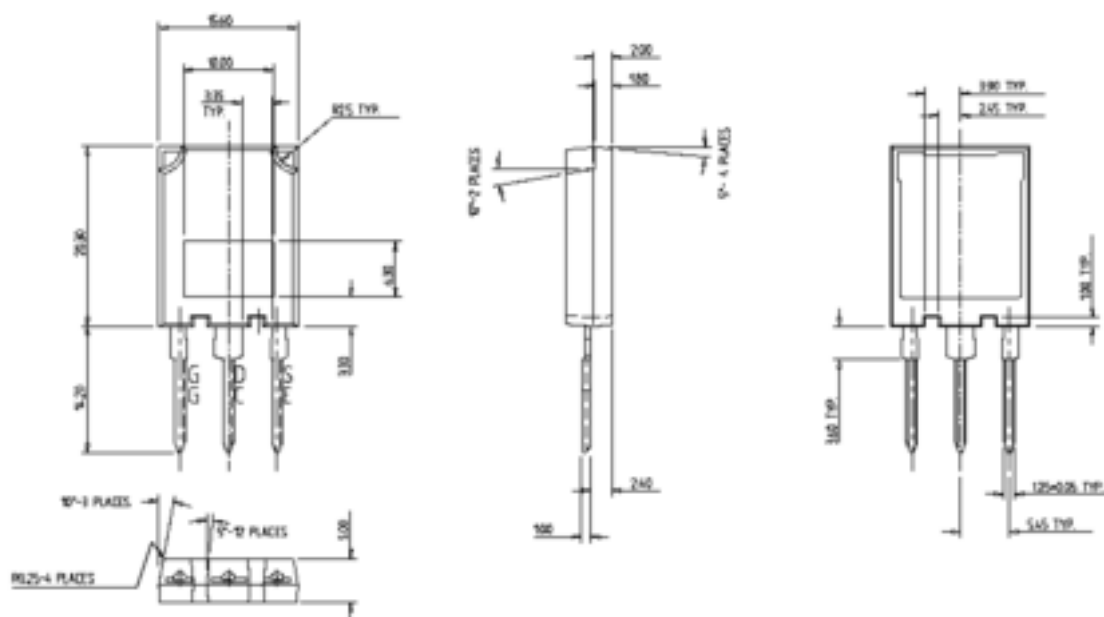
Чертеж корпуса IRGPS60B120KDP (размеры в мм.)
